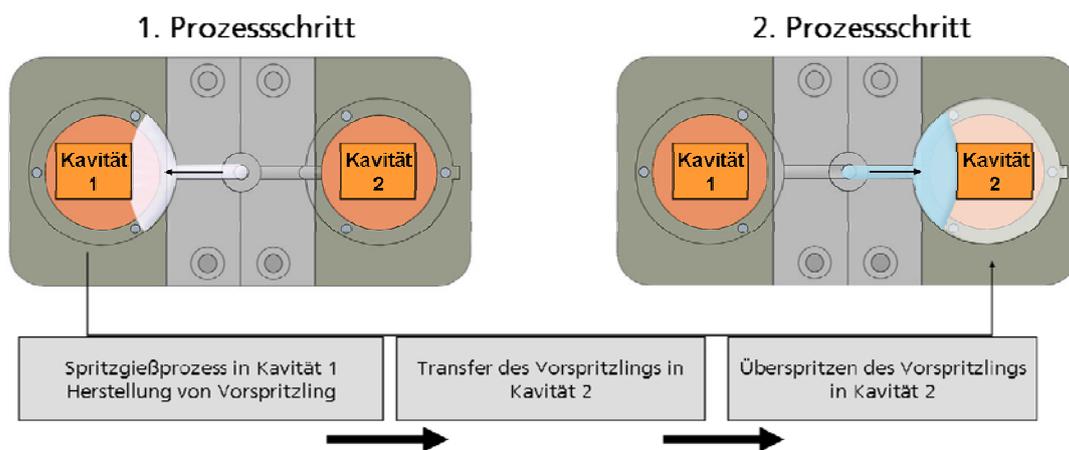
Aufbau des Versuchswerkzeugs für den Mehrschichtspritzgießprozess
